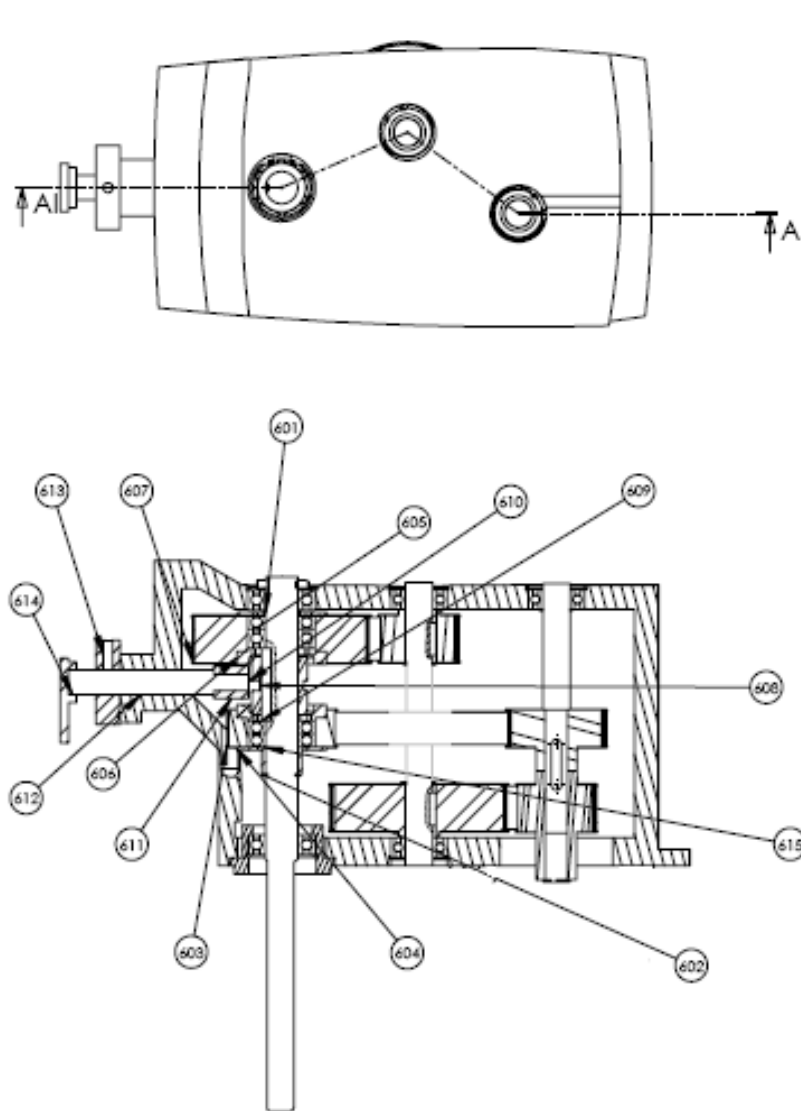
Desenho da montagem do cabeçote com mudança de gama mecânica
